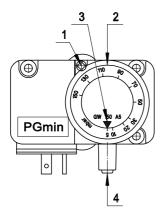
1-Винт заглушка 2-Регулировочная гайка 3-Указатель регулировки
